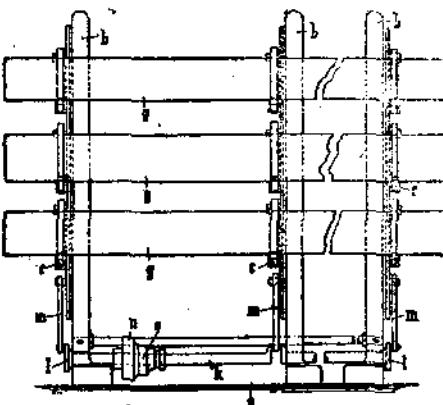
Приспособление для высушивания фанер. Боковой вид.
